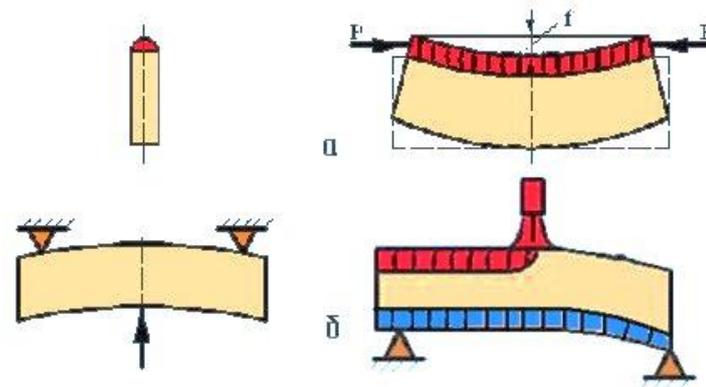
Деформация и устранение изгиба сварной заготовки:
